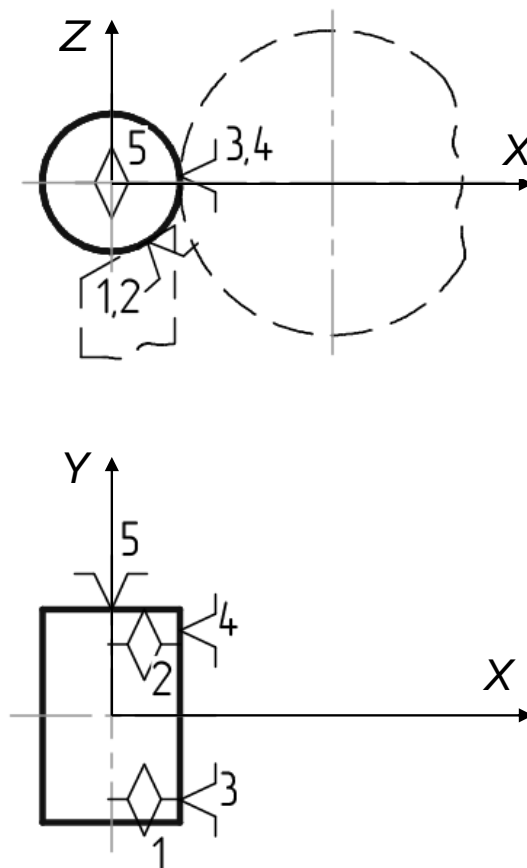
Схема базування для операцій безцентрового шліфування 020, 025, 045, 050
